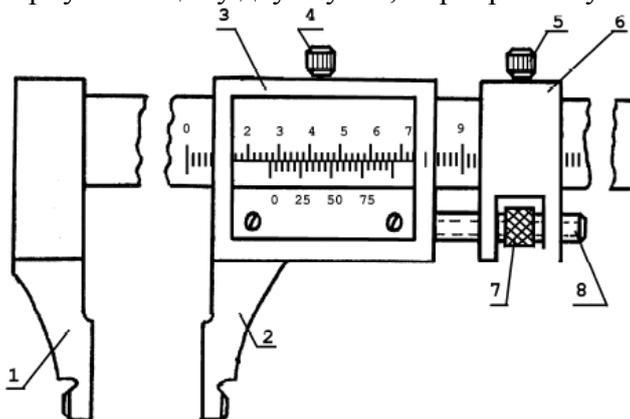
Штангенциркуль ШЦ III с односторонними губками
